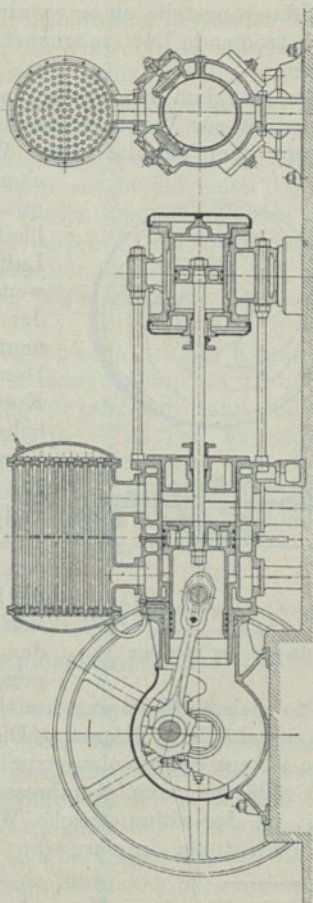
Zweistufiger Luftkompressor für Riemenbetrieb. Erfurter Maschinenfabrik Franz Beyer & Co.
